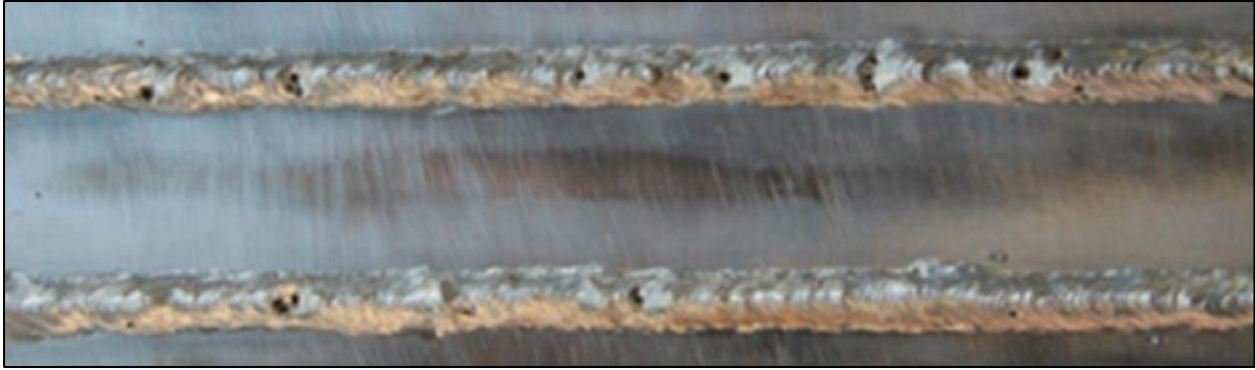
Porosidades En La Soldadura [36].
